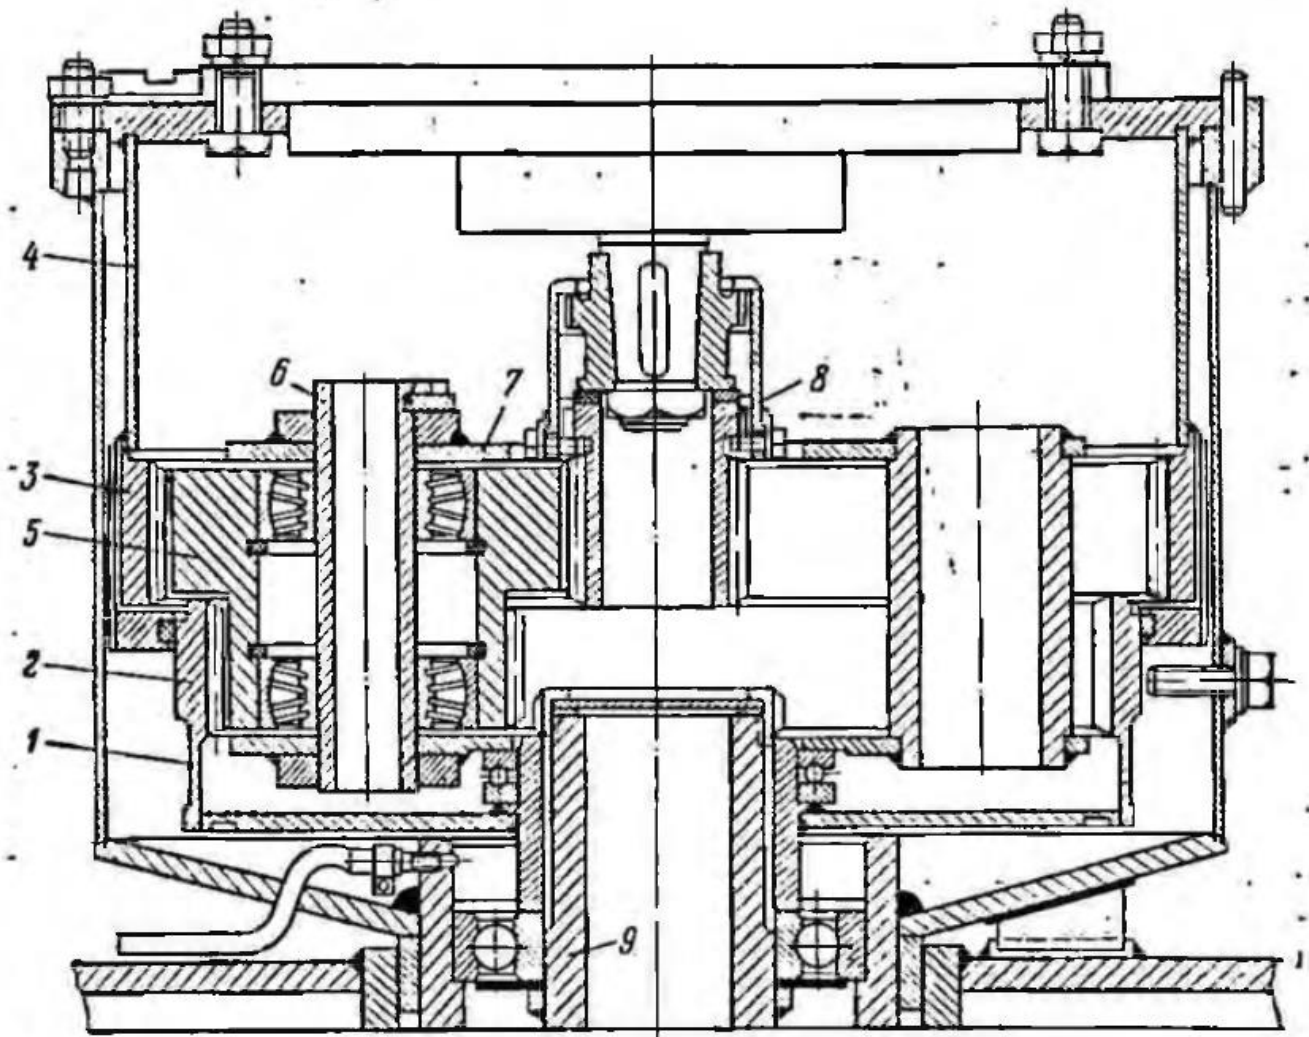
Привод механізму повороту крокуючого екскаватора [2, 5-7, 12].
